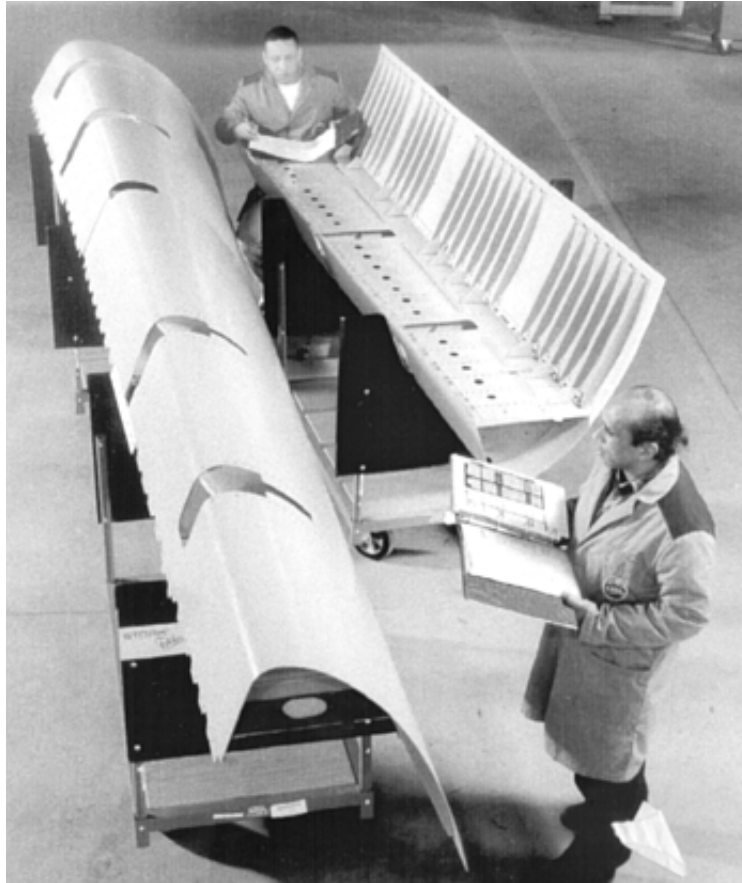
Assemblaggio del A340-500/600, ala fissa, della Fokker Aerostructures
